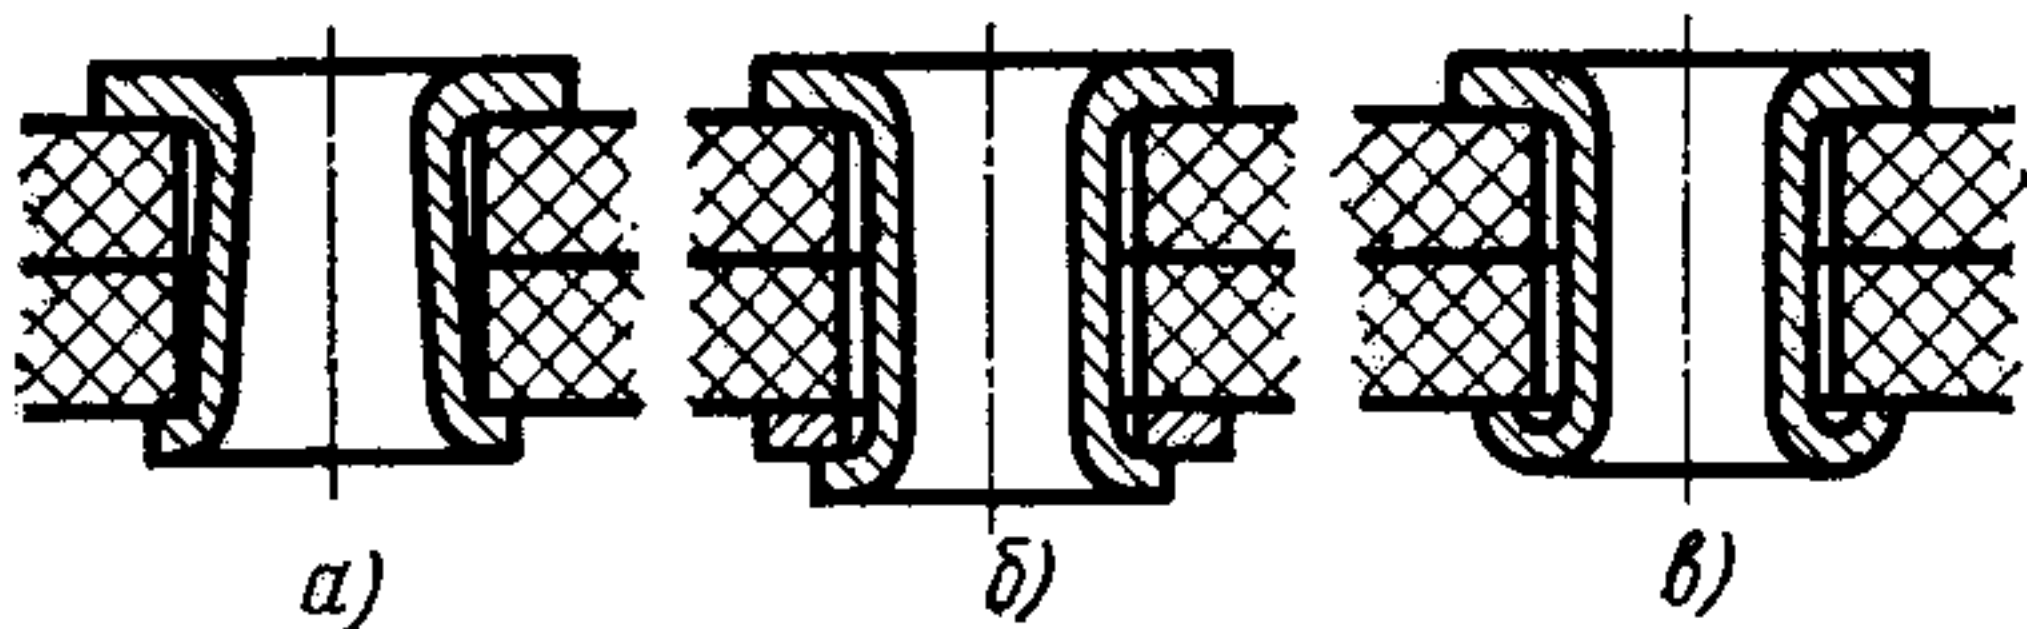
Полые заклепки для соединения пластмассовых изделий:
